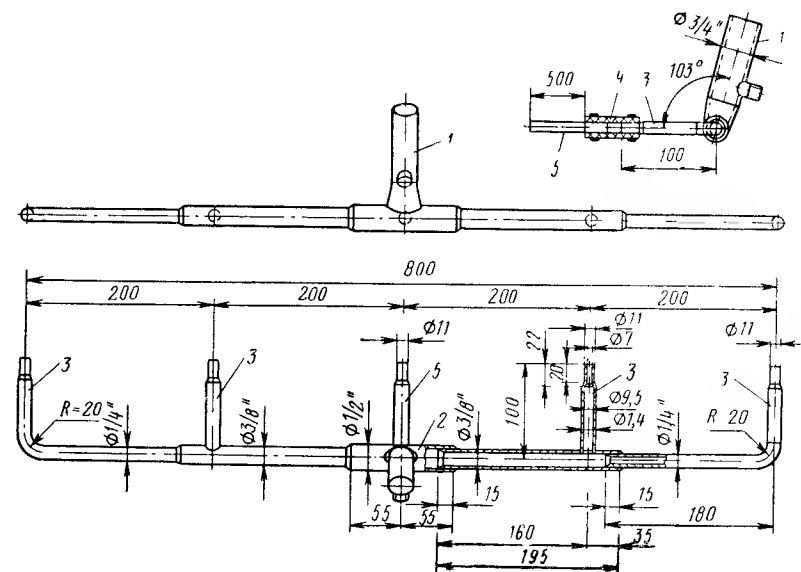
Устройство для подачи смеси газа и воздуха в камеры сгорания
